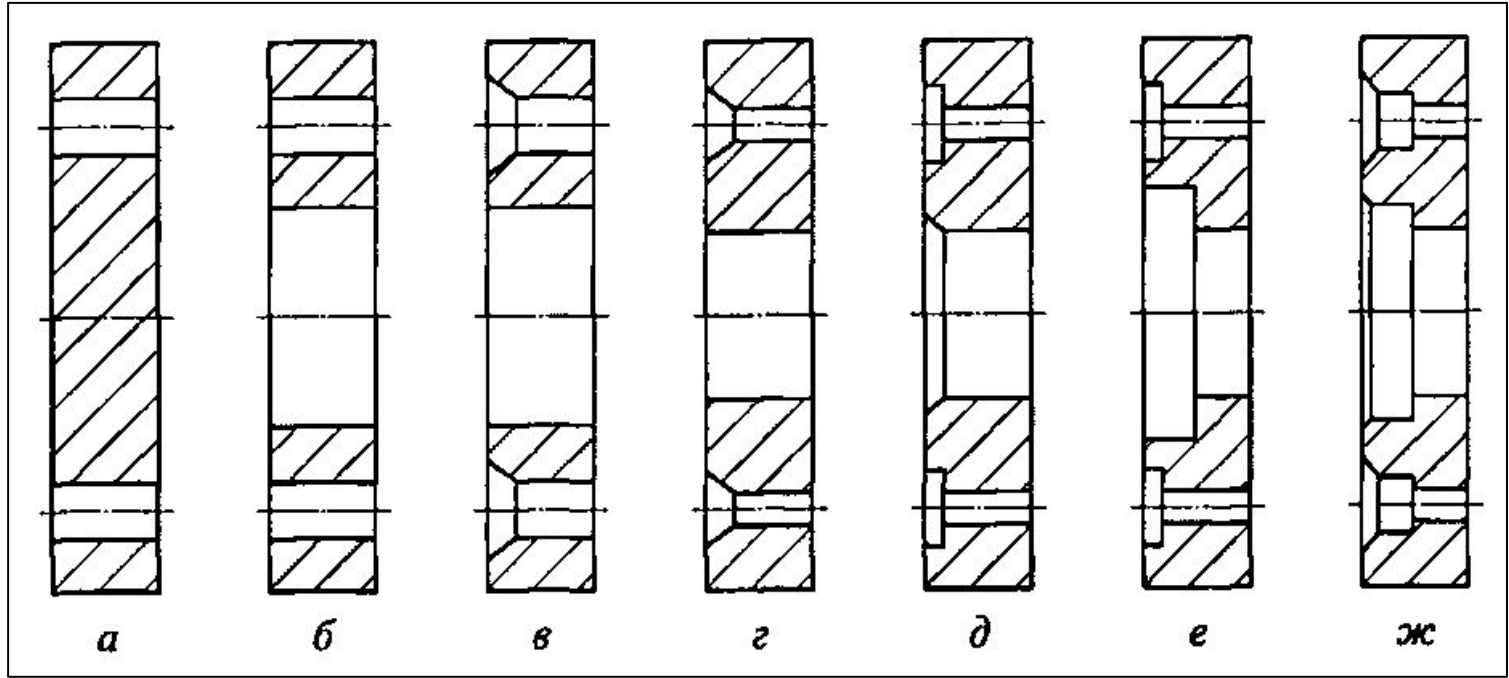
Примеры конструкций: *a—e* — детали типа фланцевого диска; *ж* — деталь-представитель
